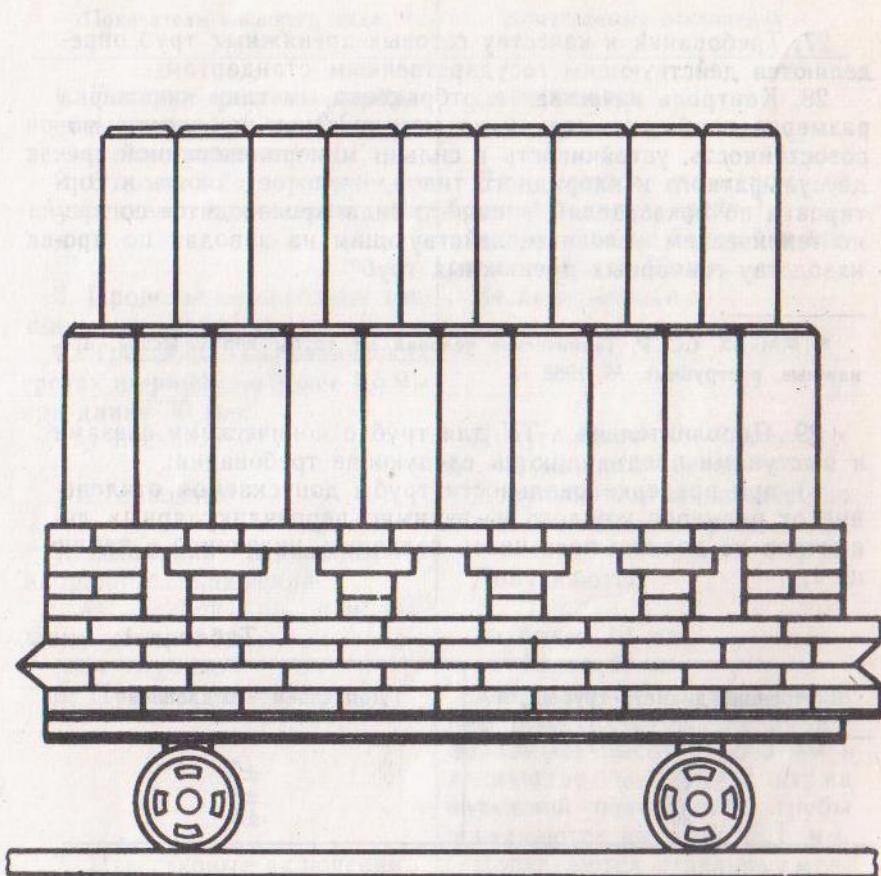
Схема садки труб на вагонетку туннельной печи для обжига.
